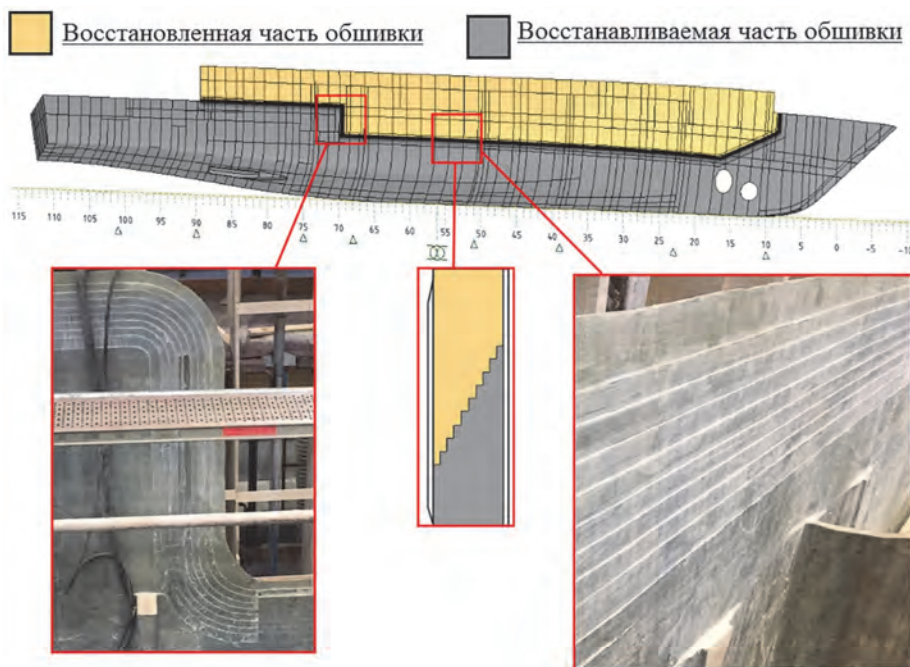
Фрагменты обшивки корпуса со ступенчатой разделкой кромок
